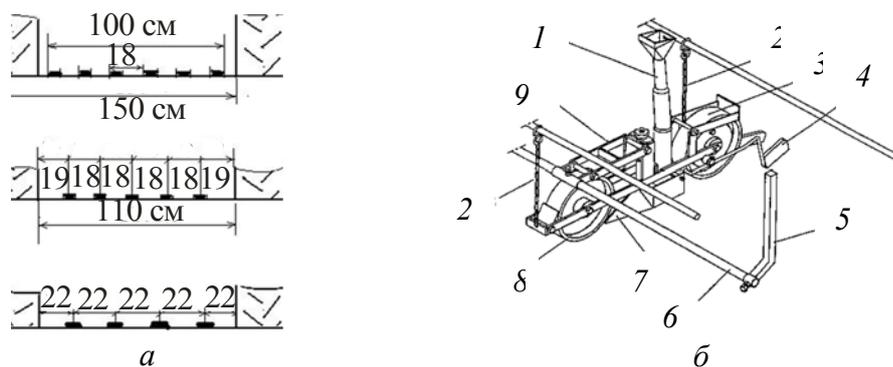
Схемы посева (а) и высевающей секции (б): 1 – семяпровод; 2 – ограничительная цепка; 3 – прикатывающий каток; 4 – загортачи; 5 – стояк; 6 – валик; 7 – сошник; 8 – копирующее колесо; 9 – тяговая рамка с механизмом установки глубины хода сошника
